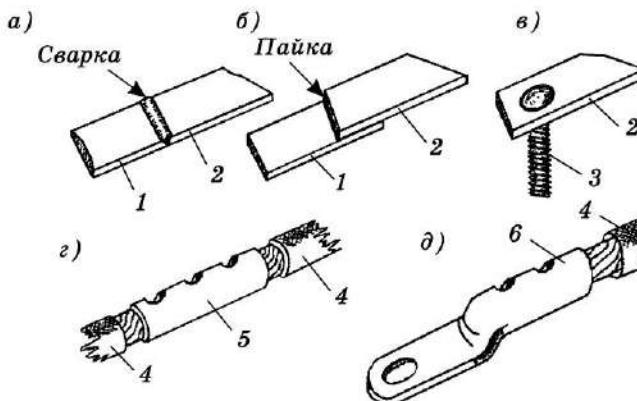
Неразборные контактные соединения: а — сваркой; б — пайкой; в — сваркой со штыревым выводом; г — опрессовкой через соединительную гильзу; д — опрессовкой с кабельным наконечником;
